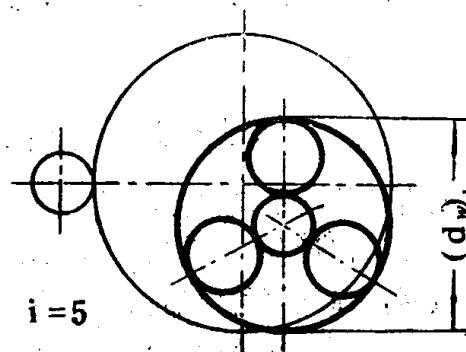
2 普通齿轮传动与行星齿轮传动的齿轮尺寸比较
